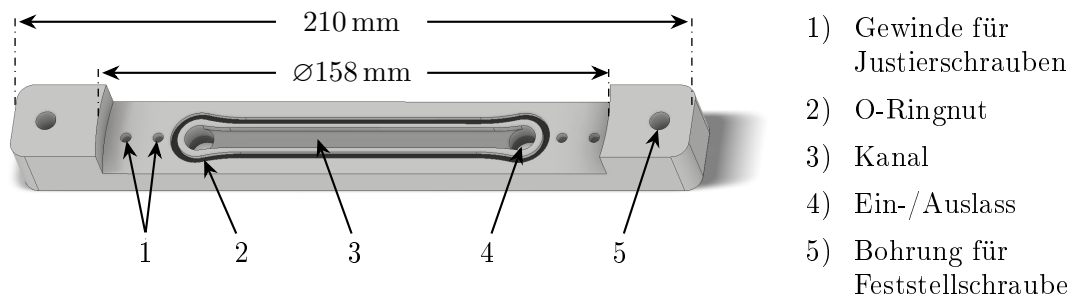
Unterseitige Ansicht der Kanalbrücke mit eingelassenem Kanal, O-Ringnut und Bohrungen für Fixier- und Justierschrauben
